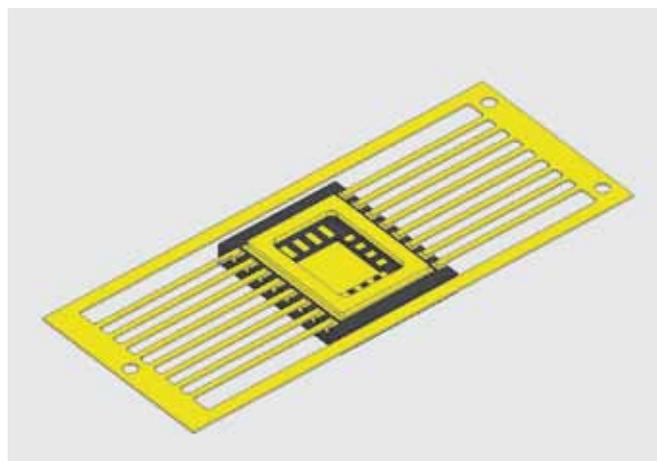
Типовой 16-выводной планарный металлокерамический корпус
